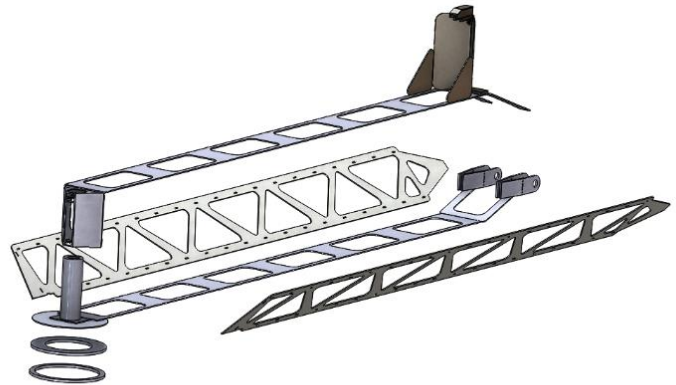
CAD - Explosionsansicht Armverlängerung
